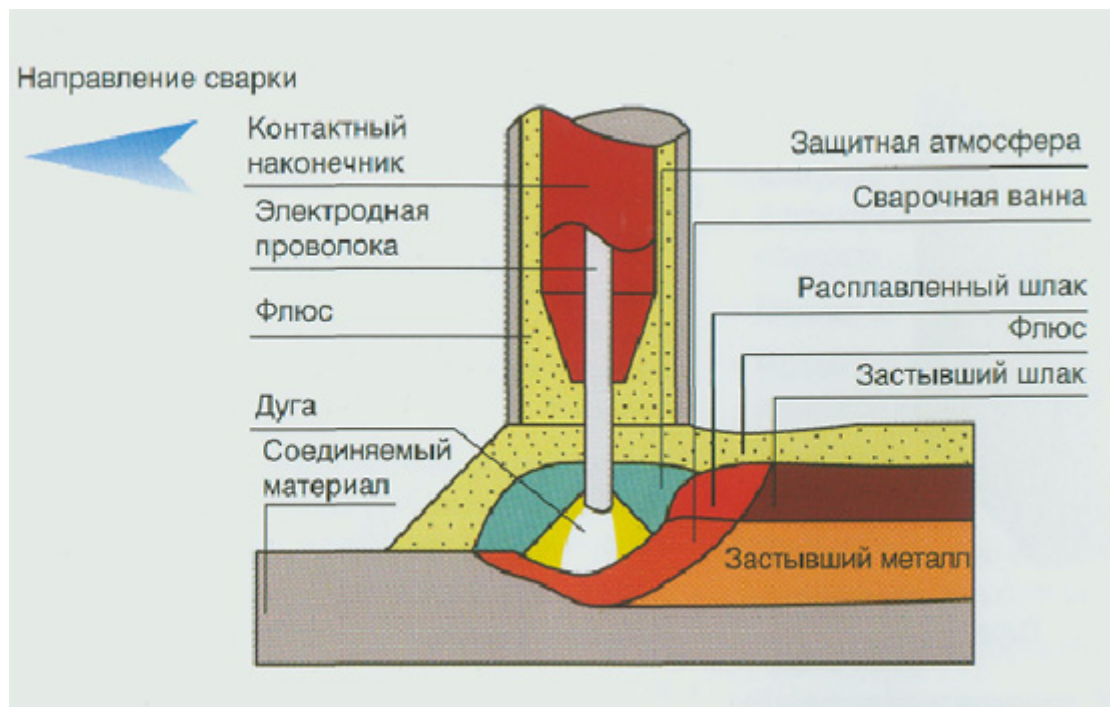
Схема автоматической сварки под слоем флюса
